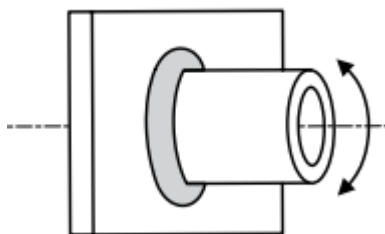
Posición de prueba para soldadura en 2FR
